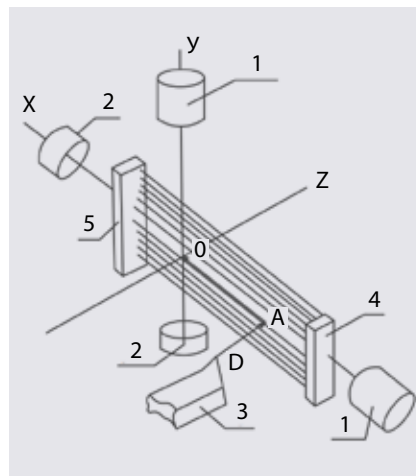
Схема автоматической настройки токарного станка с ЧПУ предлагаемым способом [5]
